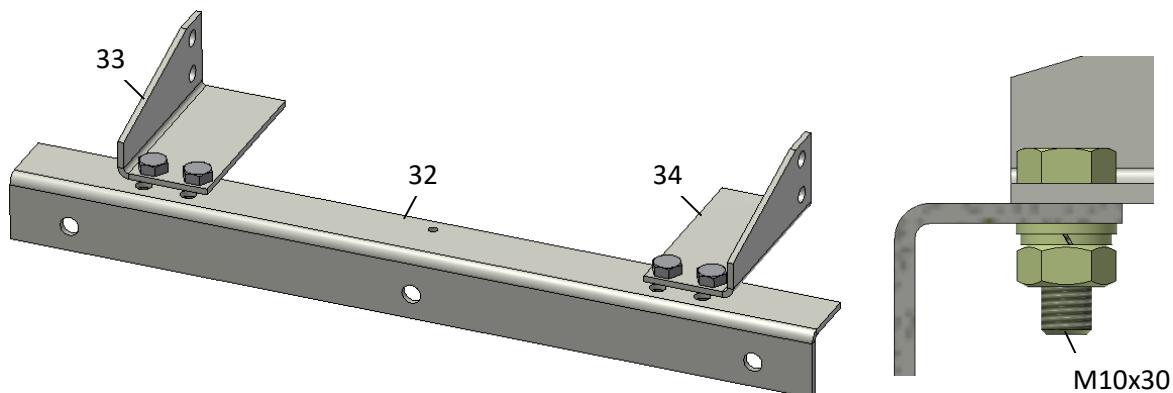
Сборка узла под нижние опорные изоляторы для ВЭ с ВМПЭ-10 или ВМПП-10
